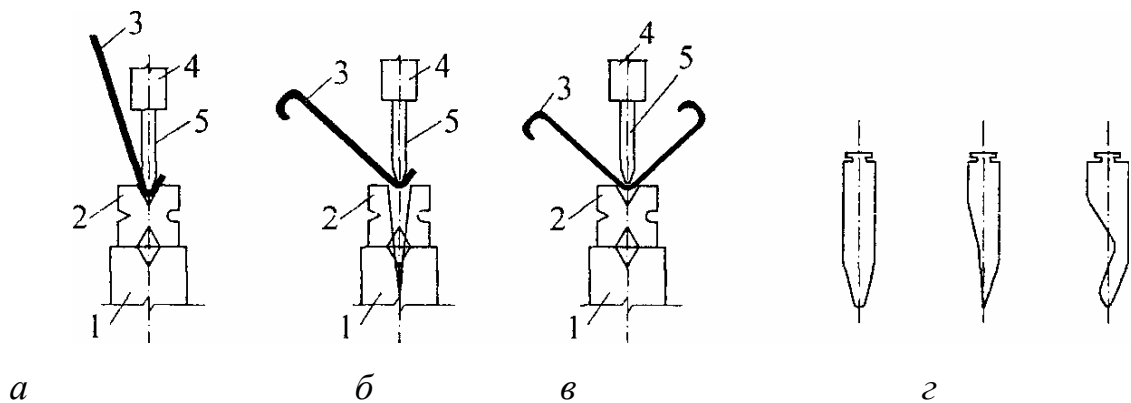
Схема виготовлення гнутих профілів на крайкозгинальному пресі: *а* - перший згин; *б* - другий згин; *в* — третій згин; *г* - форми штампів; 1 - стіл преса; 2 - нижній штамп; 3 - оброблюваний лист; 4 - повзун; 5 - верхні штаmpi
